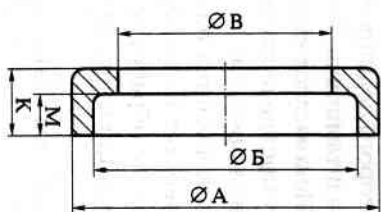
Эскиз кольцевой детали, изготавливаемой из листового материала
